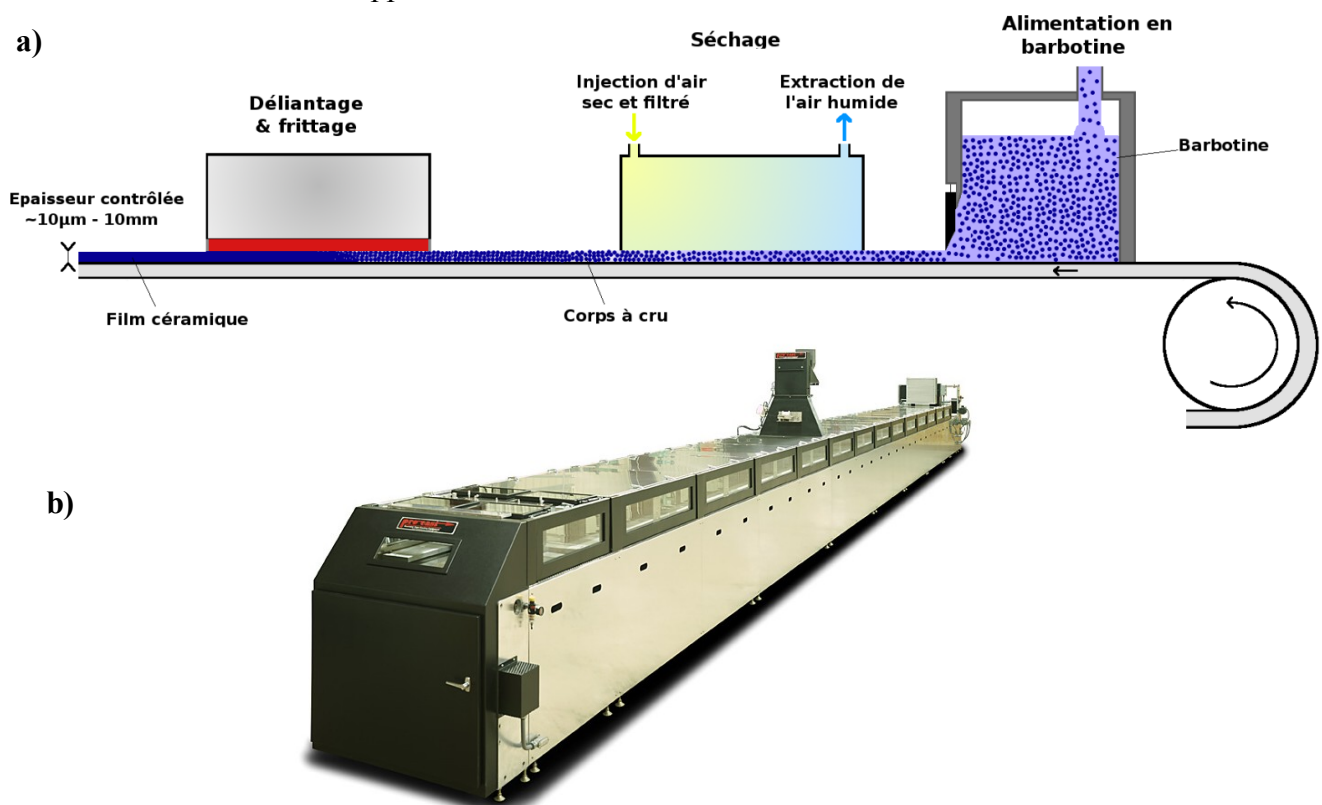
a) Principe de mise en forme par tape-casting, b) Unité de tape-casting de format industriel
